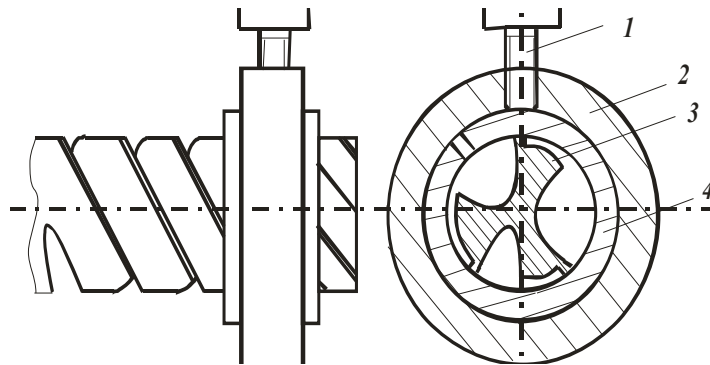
Схема доводки наружной поверхности твердосплавного многолезвийного инструмента: 1 – винт; 2 – кольцо; 3 – обрабатываемая деталь; 4 – притир [5]
